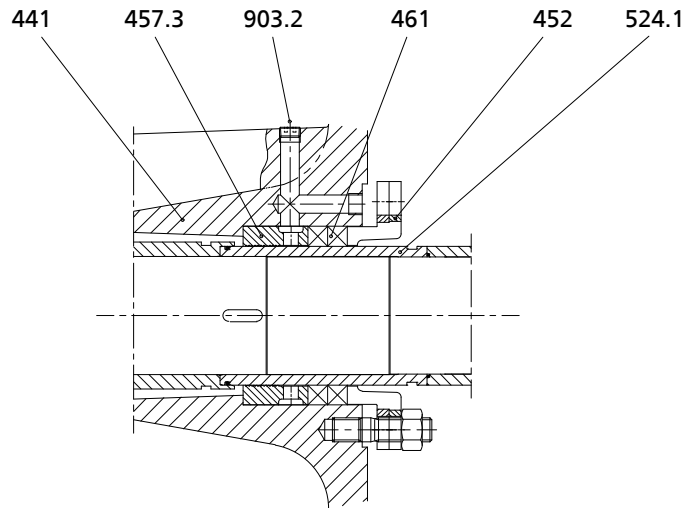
Деталировочный чертеж: Сальниковая набивка
